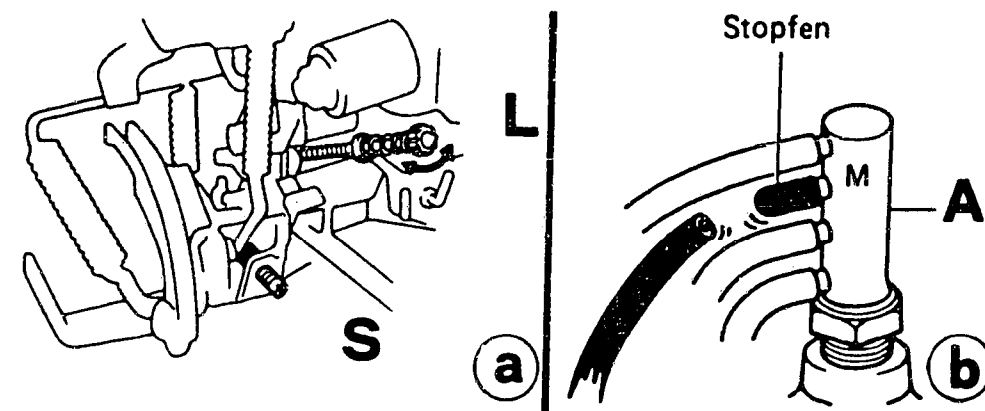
Einstellschrauben für die Leerlauf- (L) und Schnelleerlauf- (S) Drehzahl am Motor 4A-C (a). Um für die Einstellung des Schnelleerlaufs die Abgasrückführung ausser Funktion zu setzen, ist der bezeichnete Unterdruckschlauch am Thermoventil A abziehen und der Anschluss zu verschliessen.
